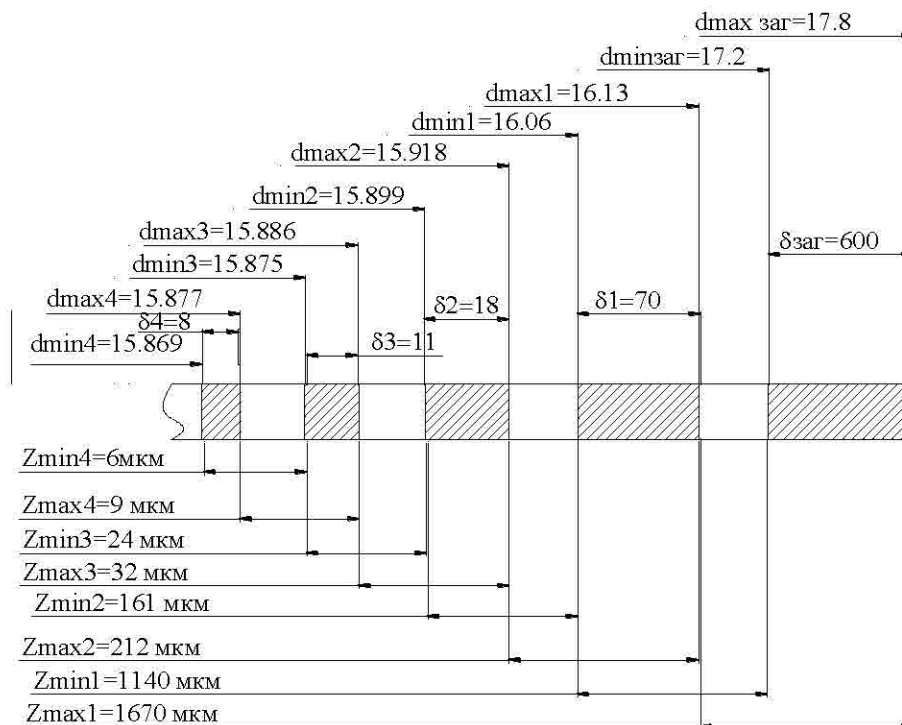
Схема графічного розташування припусків і допусків на обробку зовнішньої циліндричної  $\varnothing 15,877-0,008$
